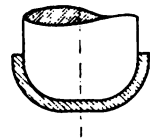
, Taf. 26, stellt den Kolben einer hydraulischen Presse dar. Die Abdichtung erfolgt durch eine lederne Manschette, welche in Fig. 185 in voller Grösse gezeichnet ist. Die Abdichtung hat hier nur gegen inneren Ueberdruck zu wirken. Das Wasser presst die beiden äusseren Cylinderflächen der Manschette an den Kolben, andererseits an die Cylinderwandung der Nuth und führt den Abschluss herbei. Der Ersatz der Manschette ist hier mit ziemlichen Umständlichkeiten verknüpft, was namentlich dann von Bedeutung wird, wenn bei lebhaftem Betrieb, hohem Druck oder infolge Ansetzung einer Kruste an der Kolbenfläche rasche Abnützung eintritt.
